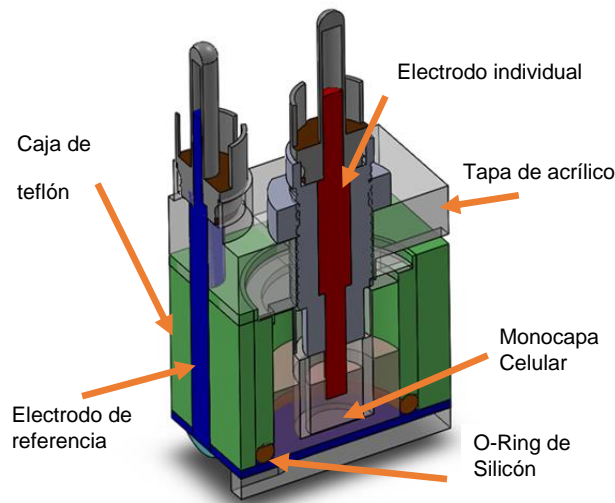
Estructura de CAMMIE con cortes en 2 planos.
